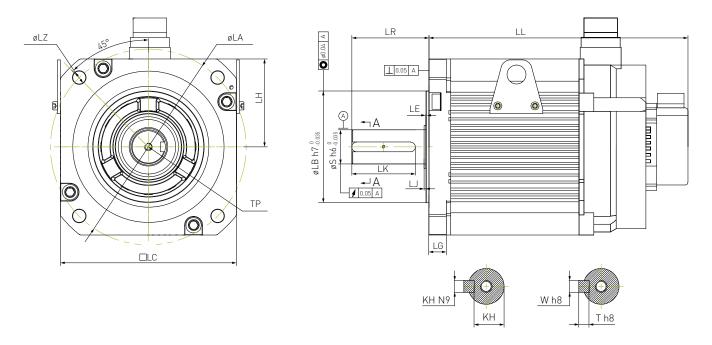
Габаритные размеры серводвигателя ELM2M-xxx (380VAC).
